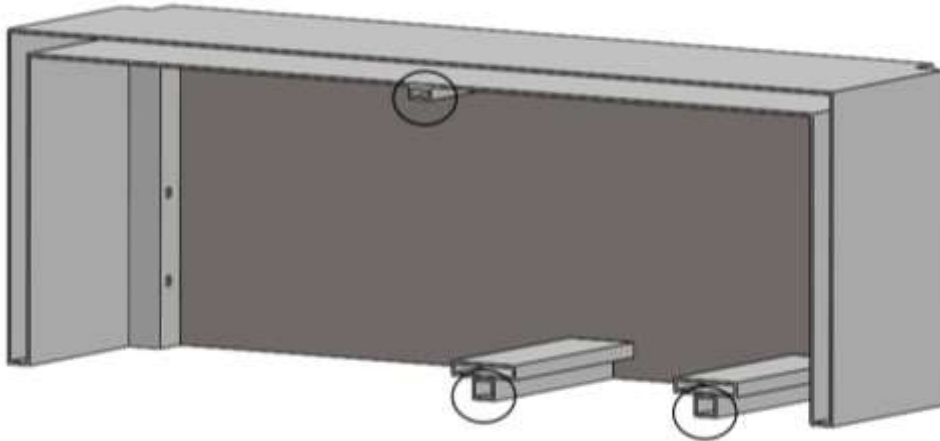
Corte alzado a sección de la estructura (Elaboración propia).
